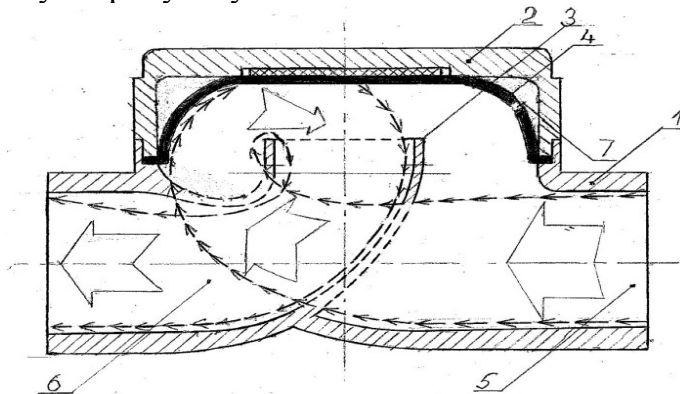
Диафрагменный клапан с опрокидывающимся потоком (двойная мёртвая петля): 1 – корпус; 2 – крышка; 3 – гнездо клапана; 4 – золотник клапана в виде резиновой диафрагмы; 5 – впускная камера; 6 – выпускная камера.
